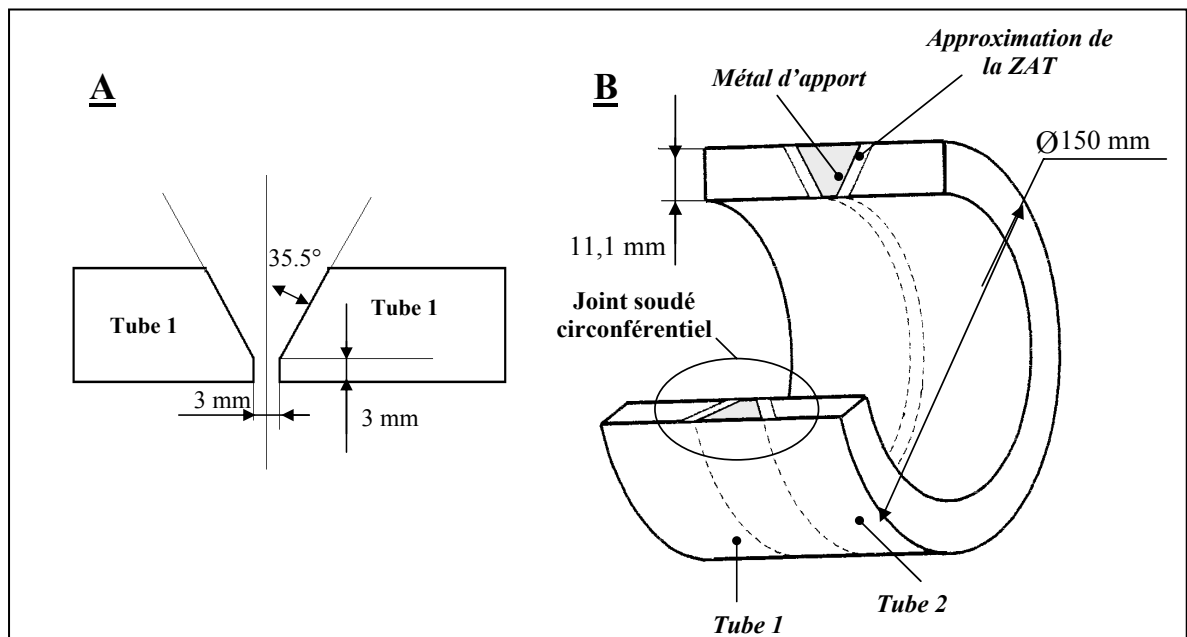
joint soudé étudié, A) le joint circconférentiel de raboutement de deux tubes. B) Géométrie de la section du joint. Le tube1 en acier martensitique, le tube2 en acier duplex.
